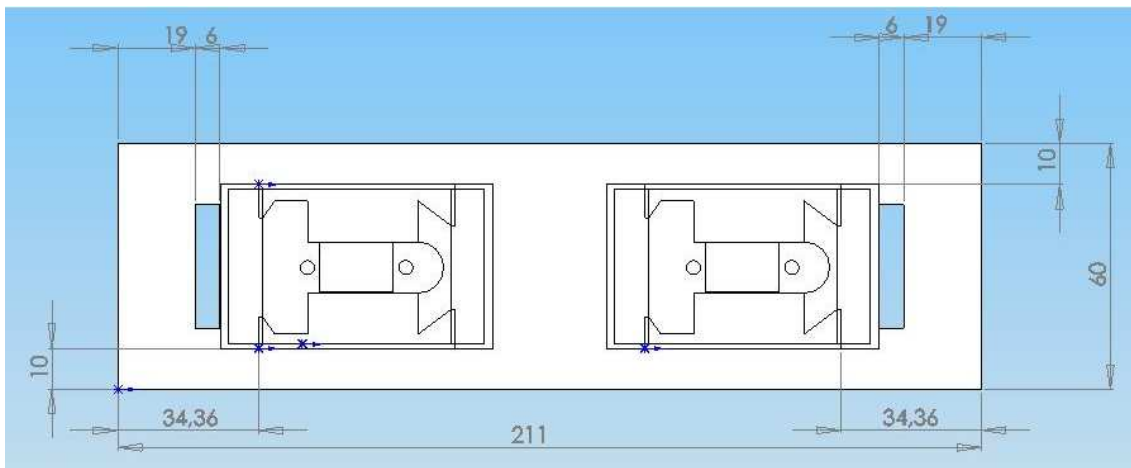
Dimensiones plancha de aluminio tubo largo.
